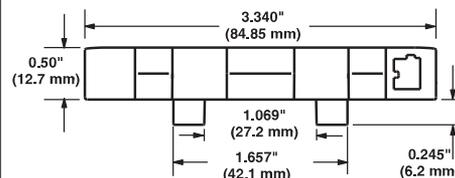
S1400 Mold to Width Flat Top de 85 mm
